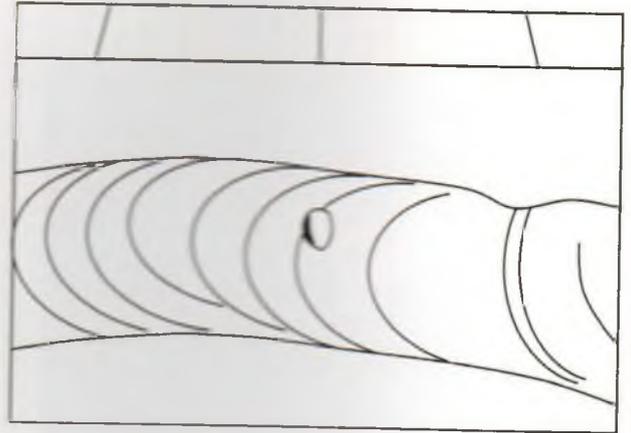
Пора в стыковом сварном соединении трубопровода
